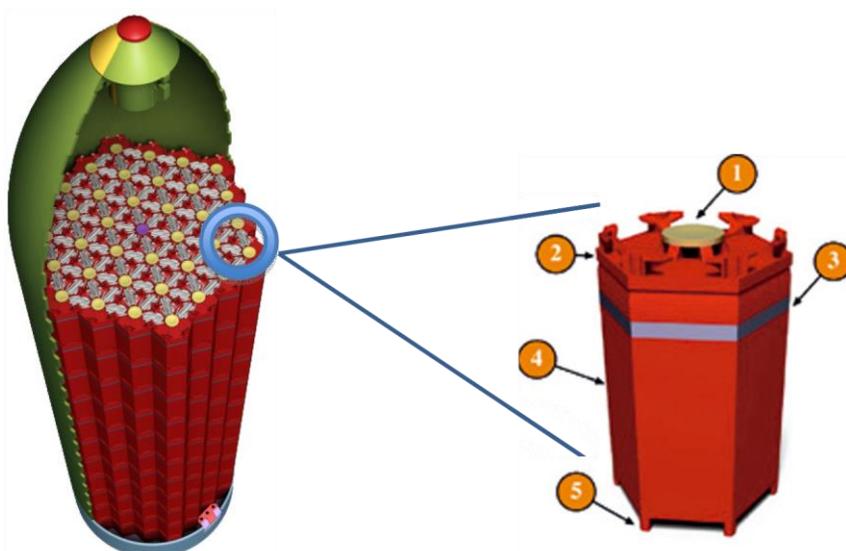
Proyectil extintor y detalle de cápsula. Fuente:[13]
